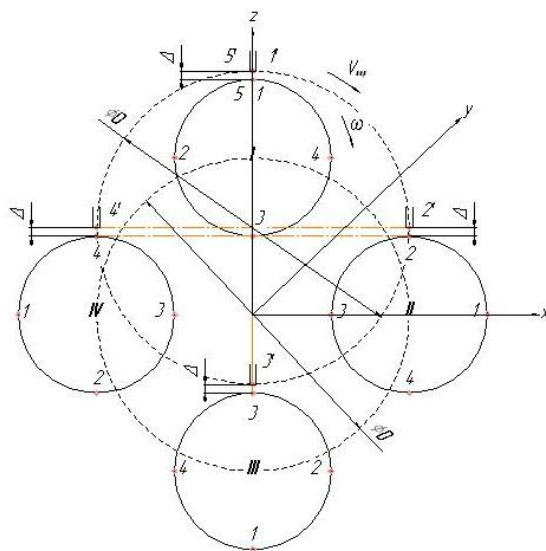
Схема движения шатунной шейки и наплавочного сопла.
